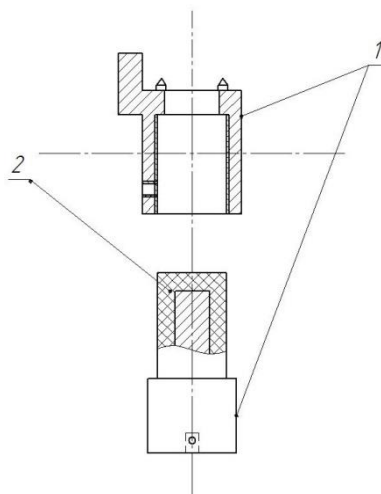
Оснастка, где: 1 - корпус детали, корпус оснастки, 2 - резиновая прокладка
